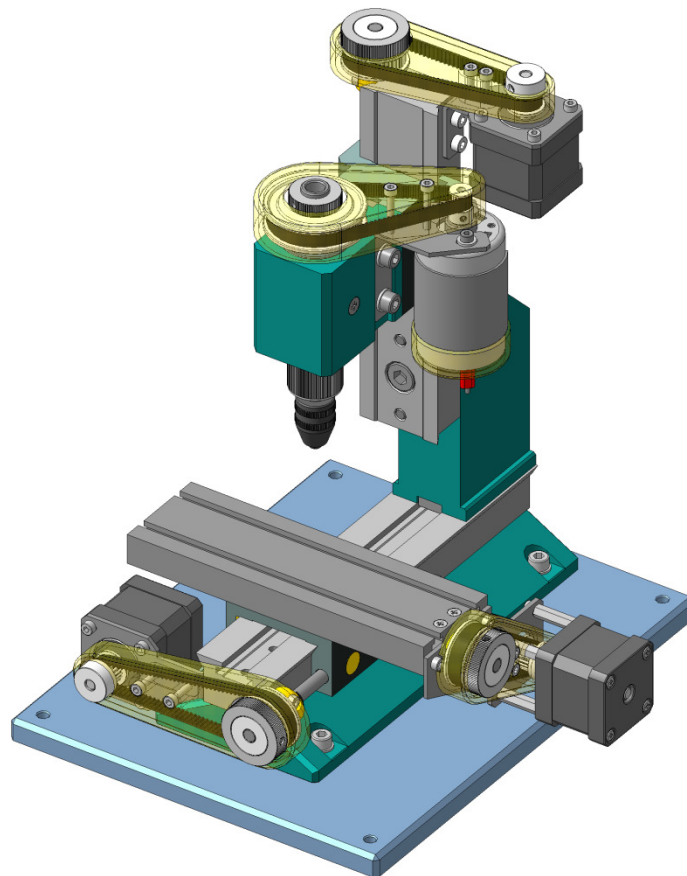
Модель компактного фрезерного верстата з ЧПК
